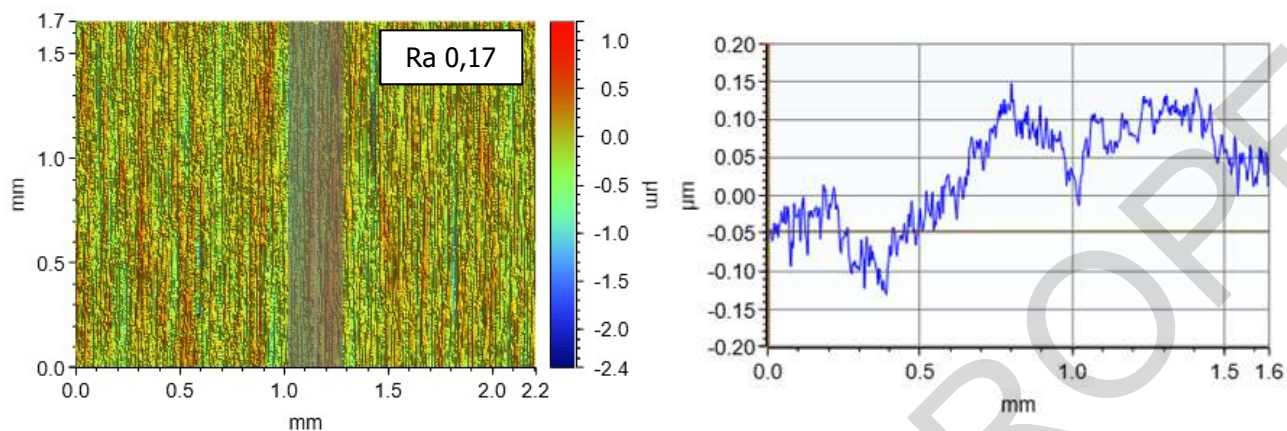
Topografie vzorku kroužku před testy „Block-on-Ring“
